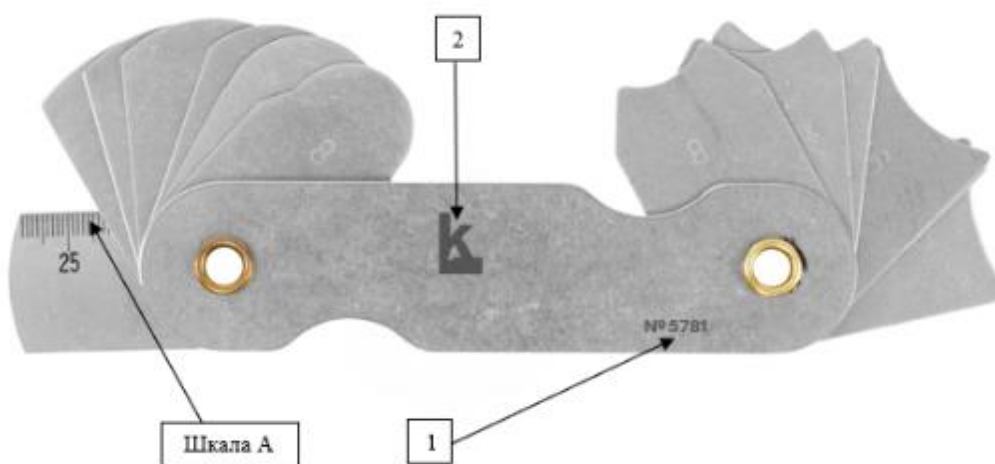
Общий вид стороны шаблона сварщика модели WGR
